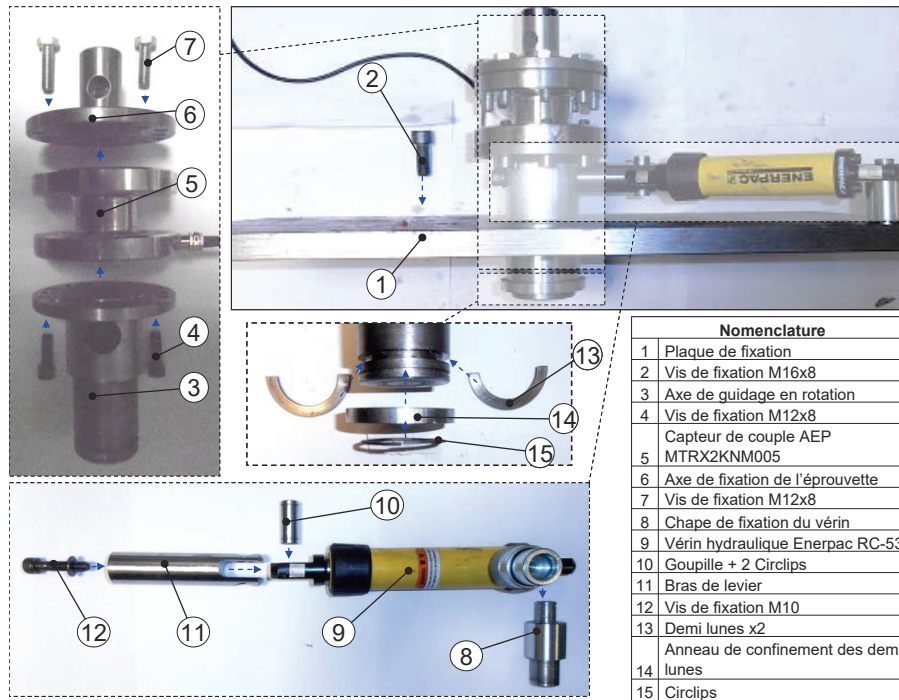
Montage de mise en torsion d'éprouvette tubulaire
